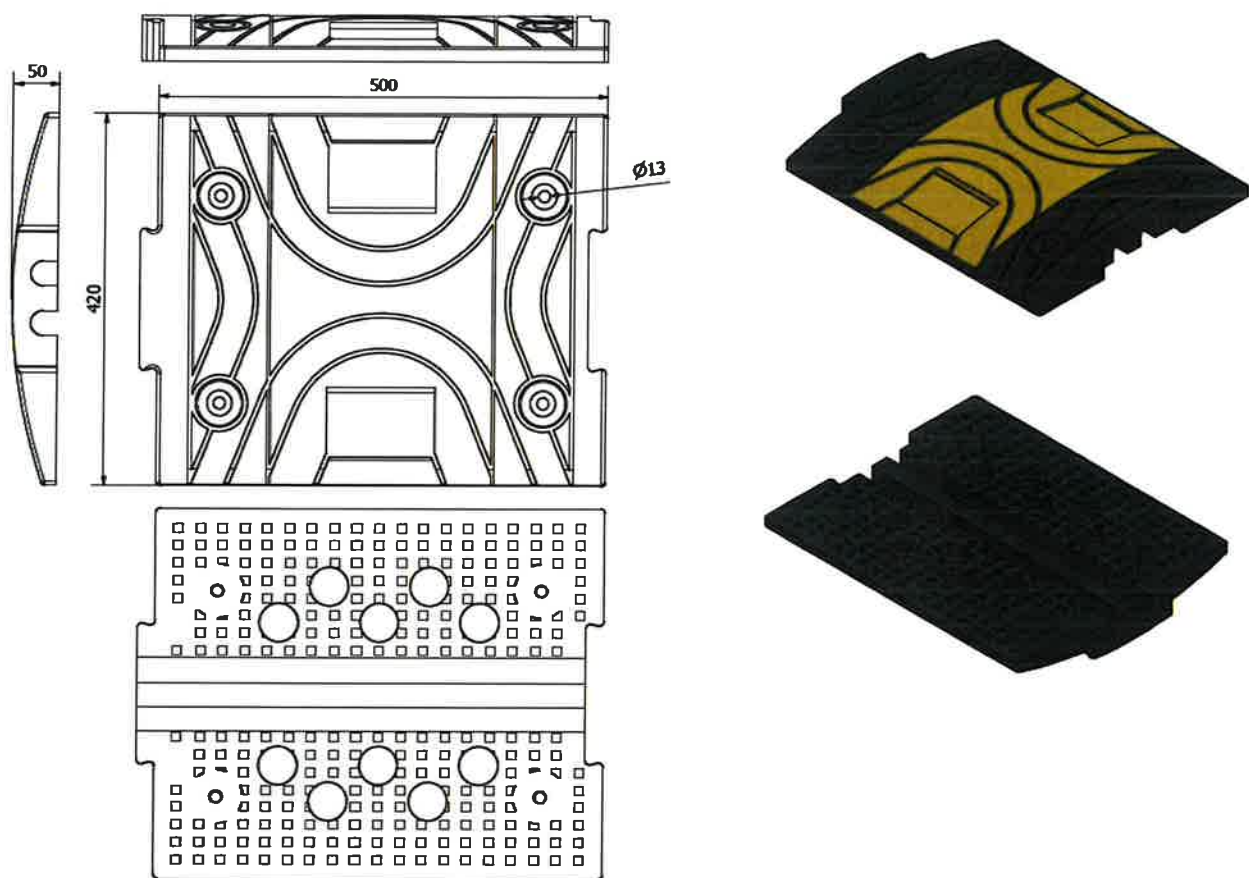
Element podstawowy progu podrzutowego PpVB-7/40
